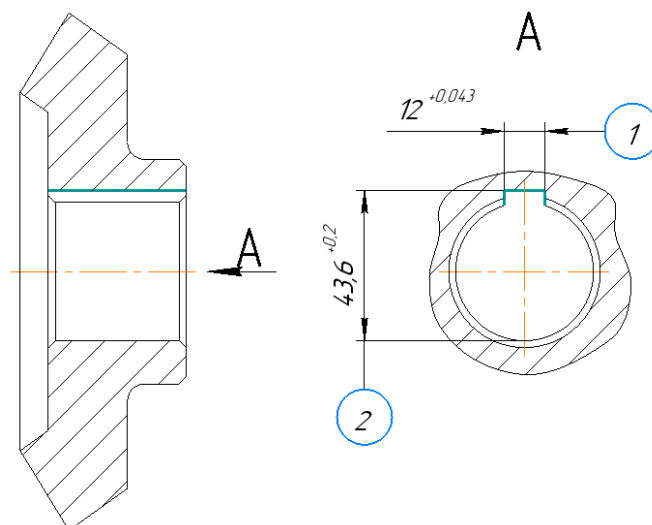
Ескіз обробки заготовки на операції 015
